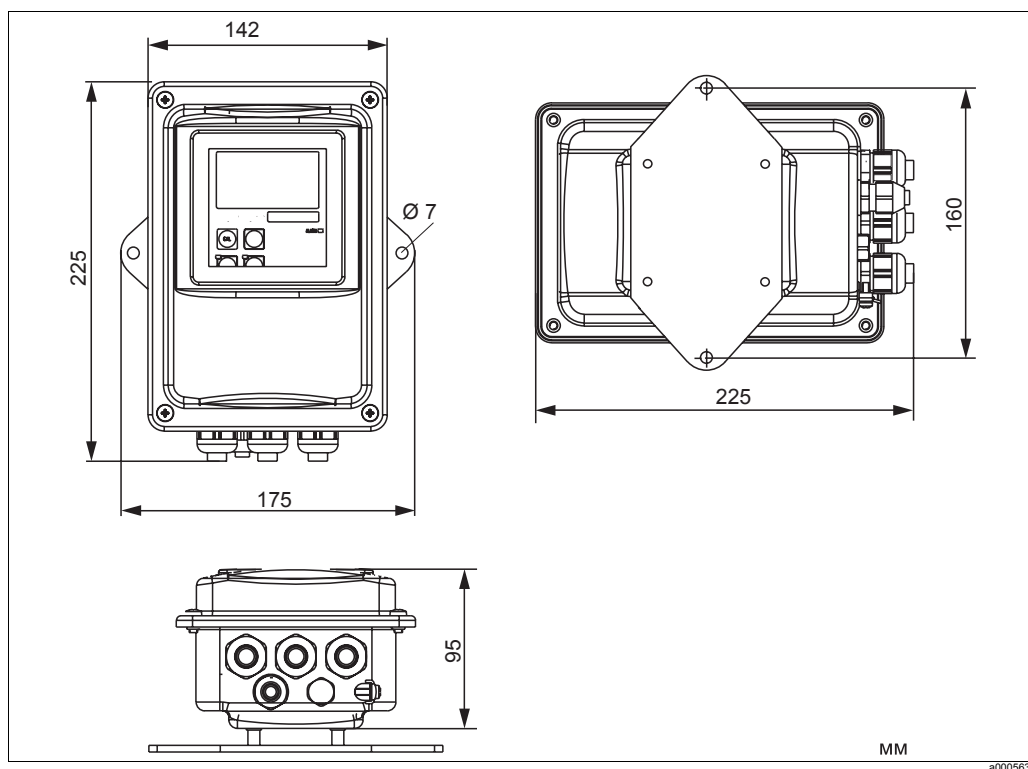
Монтаж CLD134 на стенке с использованием монтажной пластины
